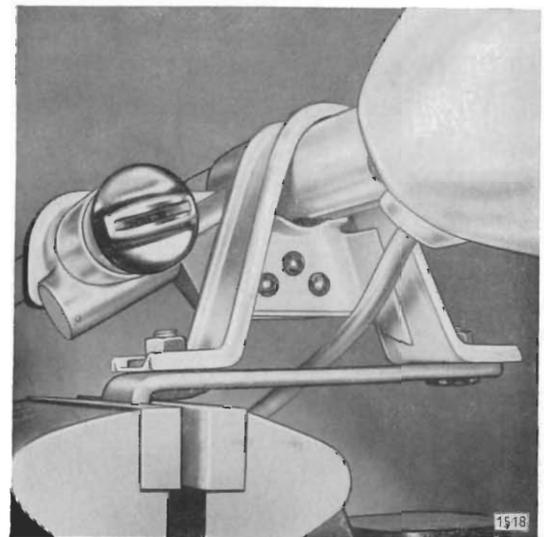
Lenkstützrohr-Zusammenbau mit Haltewinkel im Schraubstock eingespannt – im Bild Schließzylinder des Lenk- und Zündschlosses montiert
